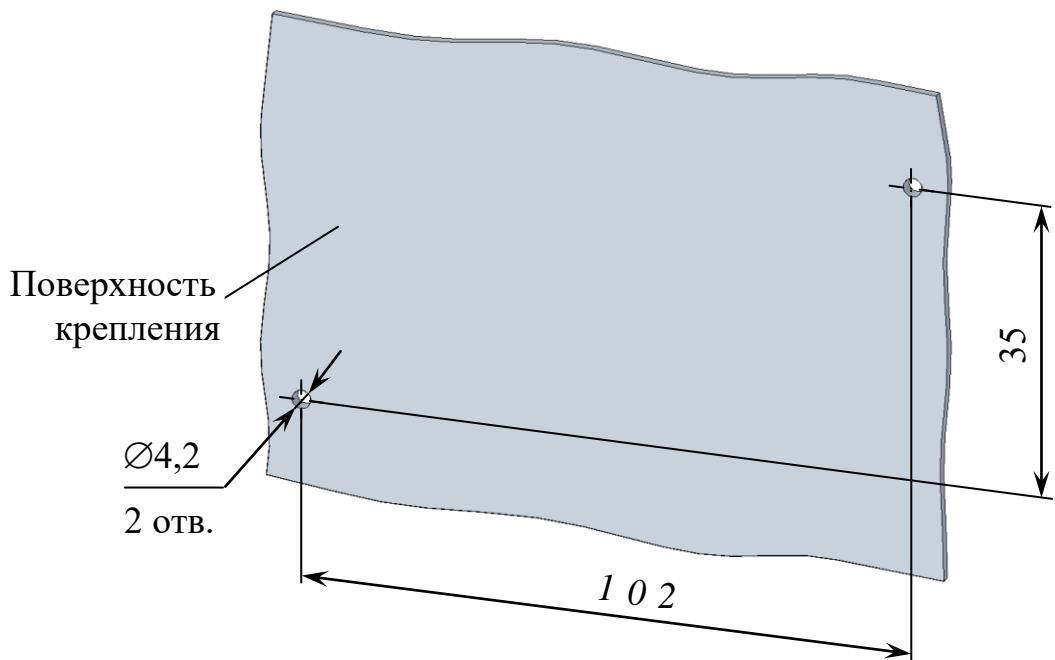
Расположение и размер отверстий для крепления коробки клеммной
